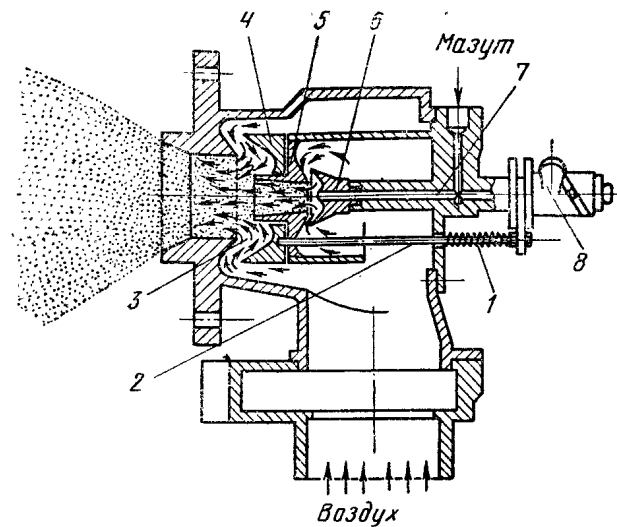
Схема работы форсунки двойного распыления типа ФДБ Союзтеплострой:
